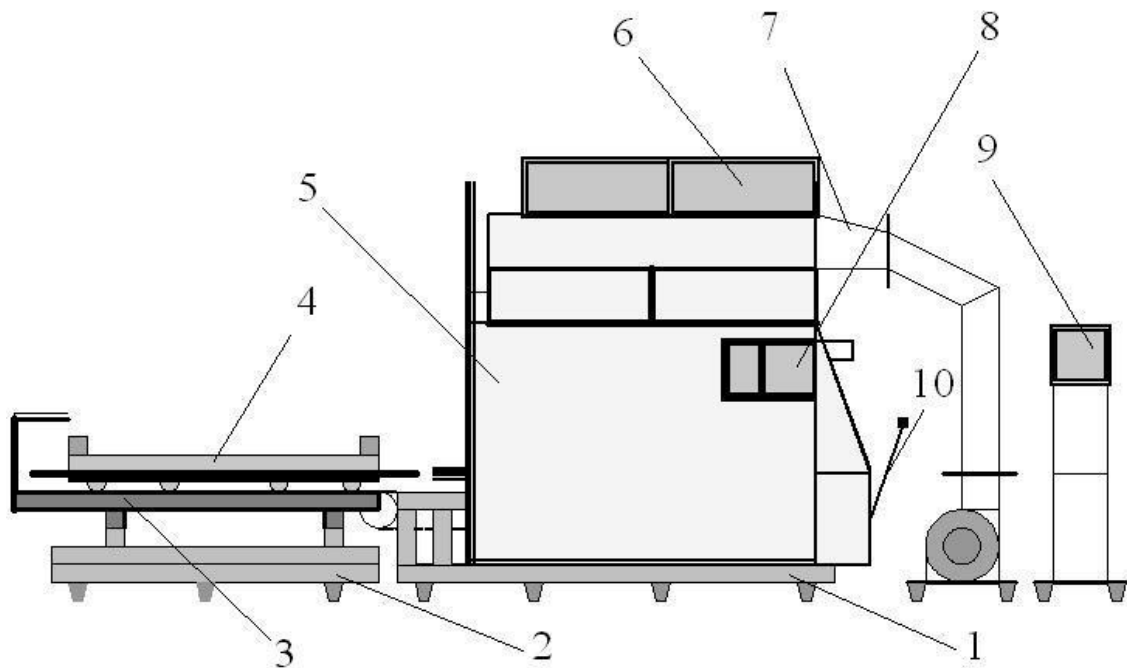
Компоновочная схема СВЧ-установки УМБ1Э [77]: 1 – станина; 2 – платформа; 3 – поперечная тележка; 4 – рабочая тележка; 5 – камера-модуль бакелизации; 6 – БЗР; 7 – система обдува; 8 – пульт управления; 9 – прибор регистрирующий "Диск- 250"; 10 – устройство подключения термопар
